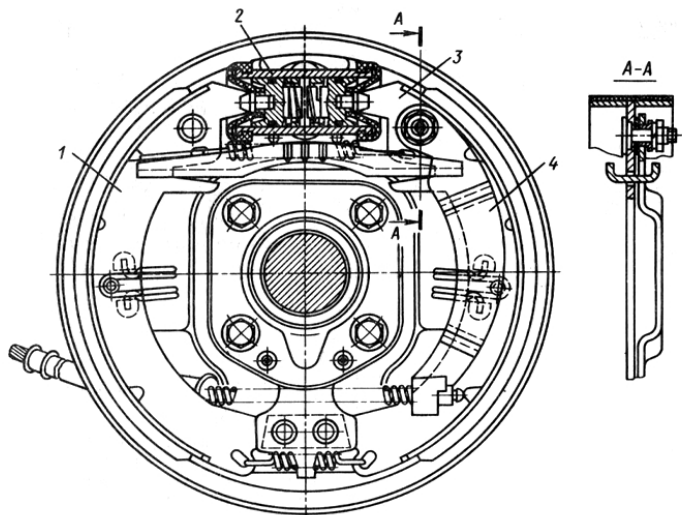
Конструкция тормозного механизма с одним цилиндром и двумя степенями свободы: 1 — передняя колодка; 2 — гидроцилиндр; 3 — задняя колодка; 4 — рычаг стояночного тормоза
